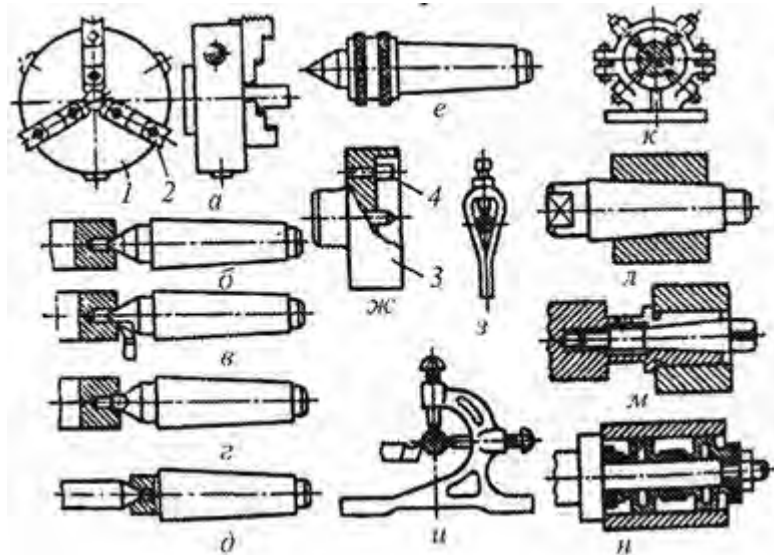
Пристрої для закріплення заготовок на токарних верстатах
